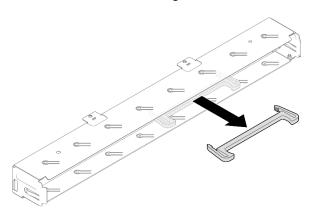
Beschaffen des Werkzeugs zur DIMM-Entfernung
